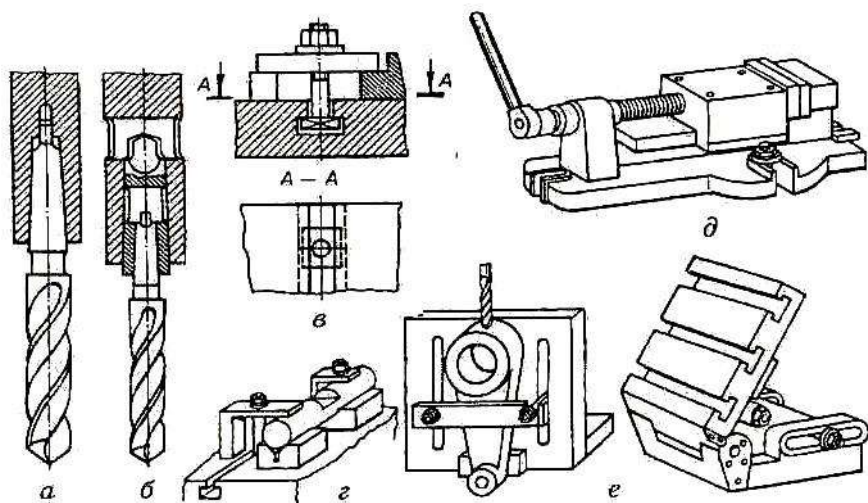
Кріплення інструменту та заготовок на свердильних верстатах
